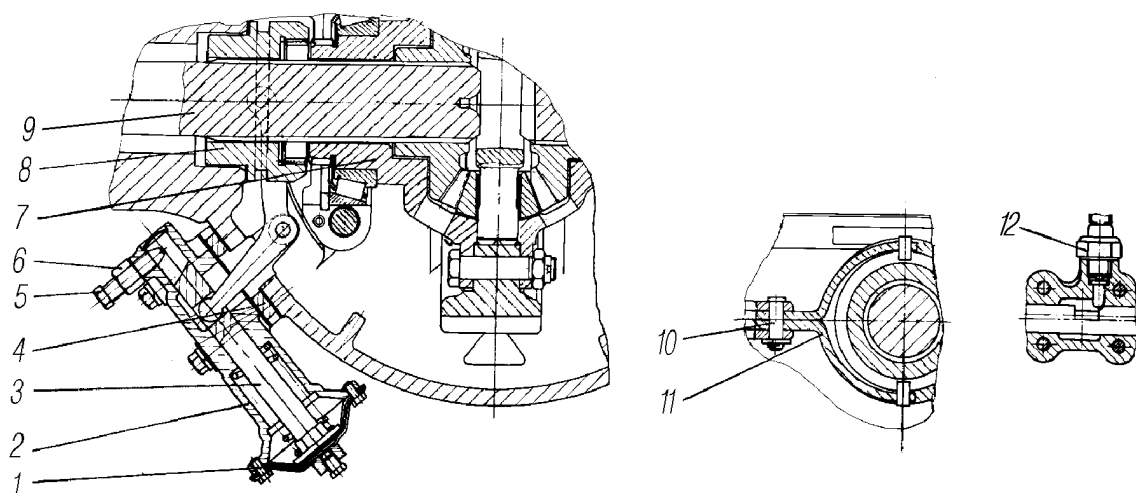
Дифференциал межколесный заднего моста с принудительной блокировкой: 1-диафрагма; 2-корпус механизма включения блокировки; 3-шток; 4-кронштейн; 5-ограничитель; 6-гайка; 7-чашка дифференциала; 8-муфта; 9-полуось; 10-палец; 11-вилка; 12-выключатель ВК403А
